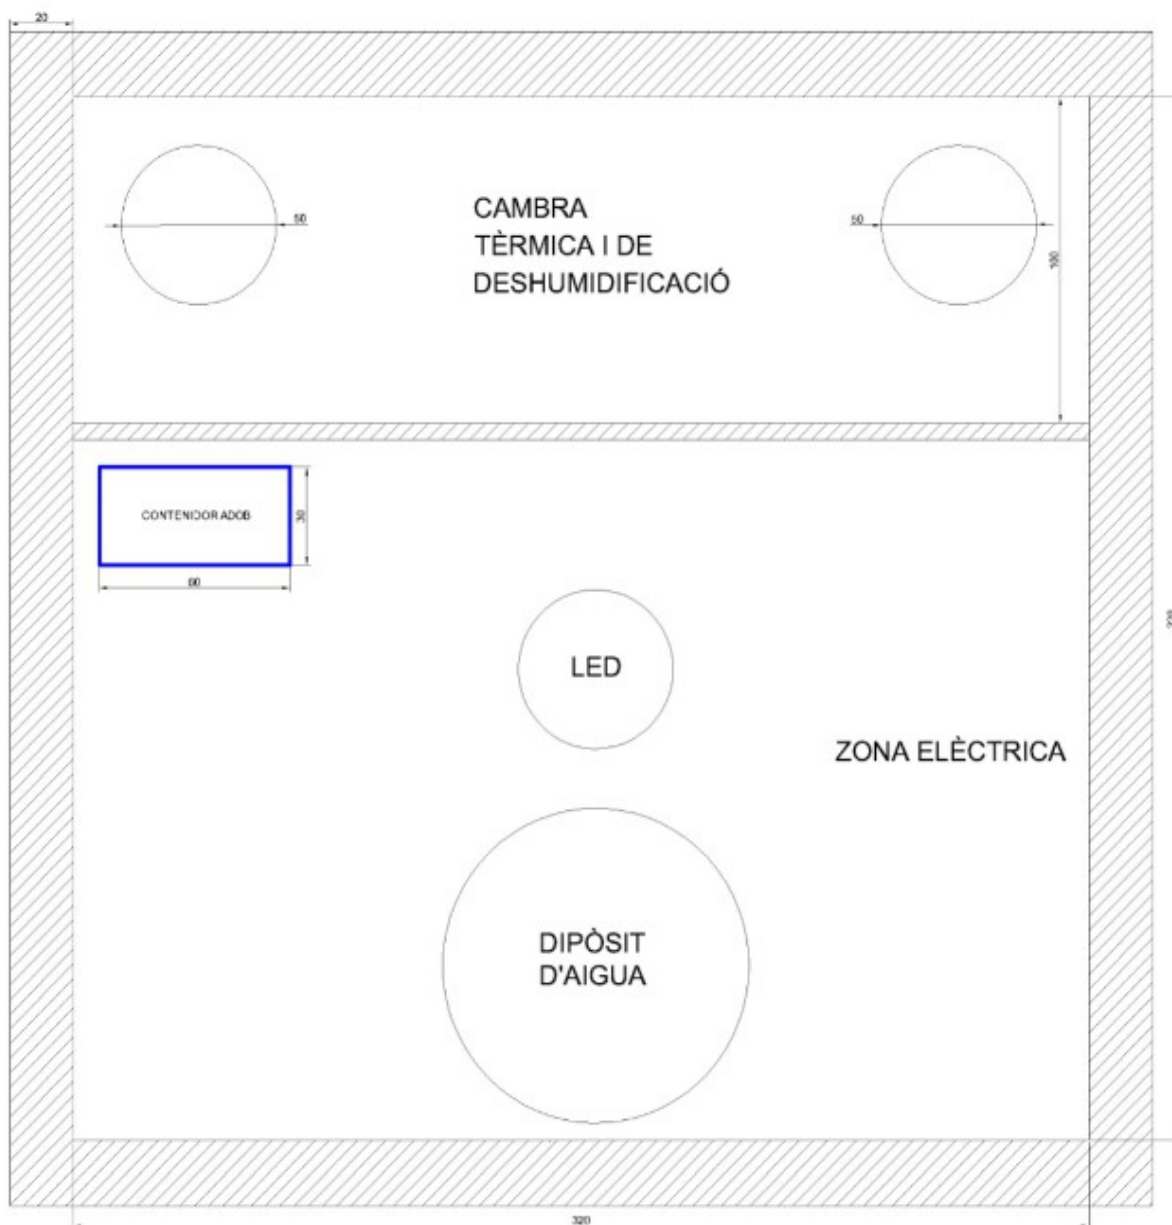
Vista de la planta de la distribució dels mòduls. Elaboració pròpia. Totes les cotes en mm.
